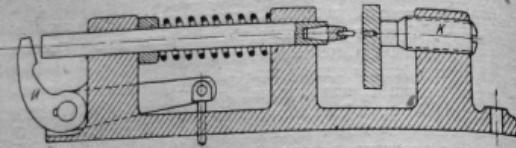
Вертикальный пресс для запрессовки штифтов.
